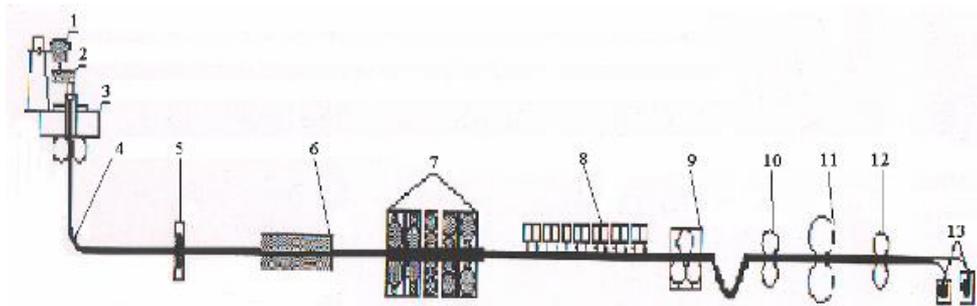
Схема расположения оборудования двухвалкового литейно-прокатного агрегата для производства тонкой жести
